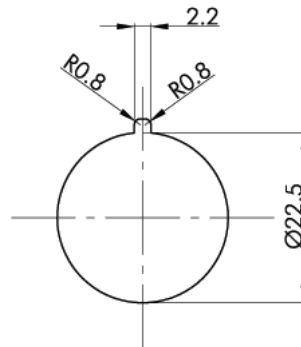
Maße der Einbauöffnung/Dimensions for the mounting cutout/Cotes de l'ouverture de montage
